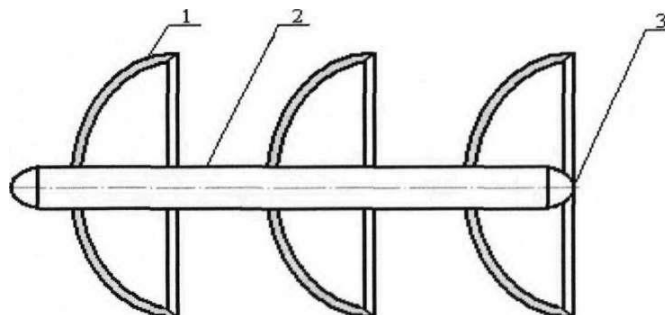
Схема механического разделителя жесткой конструкции: 1- манжета, 2 – металлический цилиндр, 3 – сферическая заглушка
